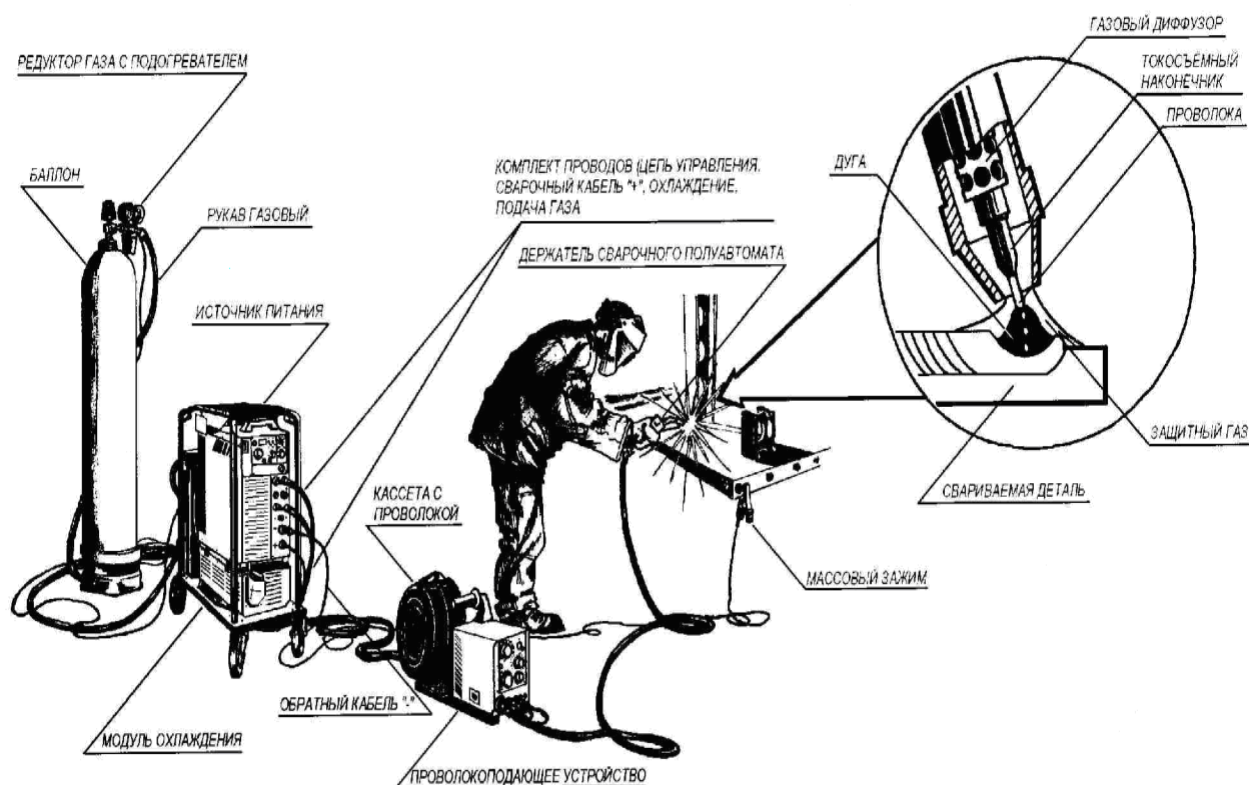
Пост для полуавтоматической сварки
